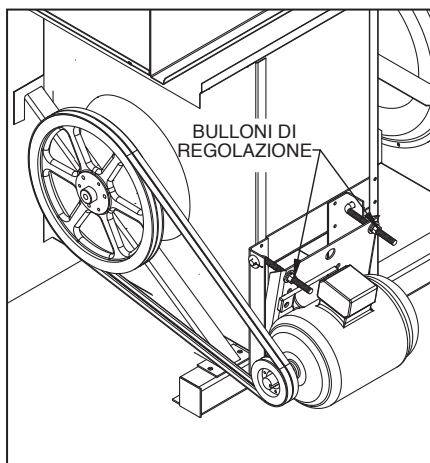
Motore esterno, unità LS, 8X e 3M di piccole dimensioni
